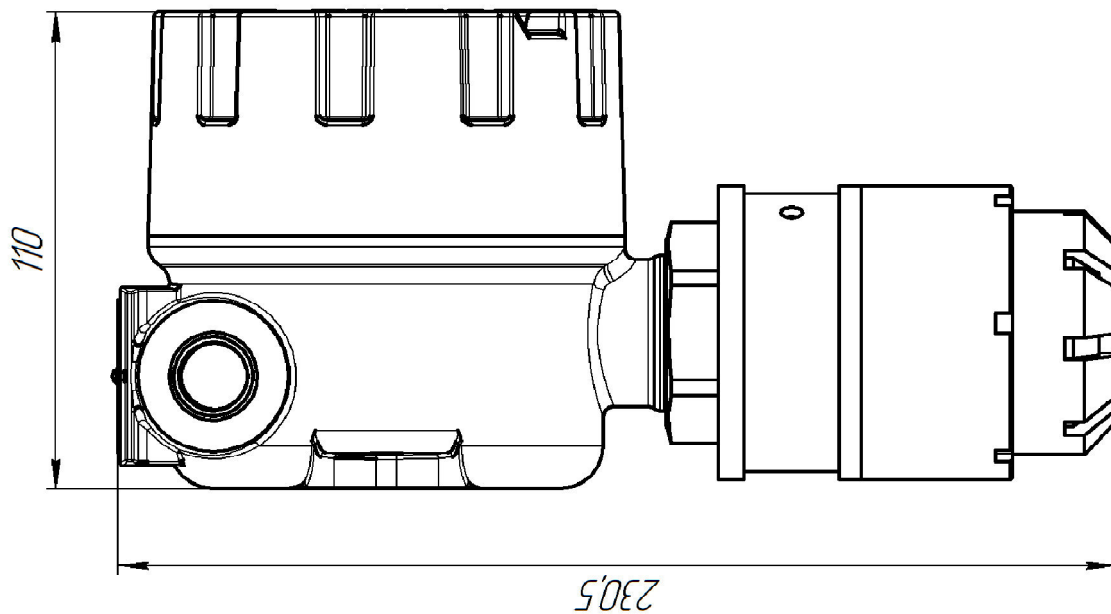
Габаритный чертеж ДГС ЭРИС-ФИД
